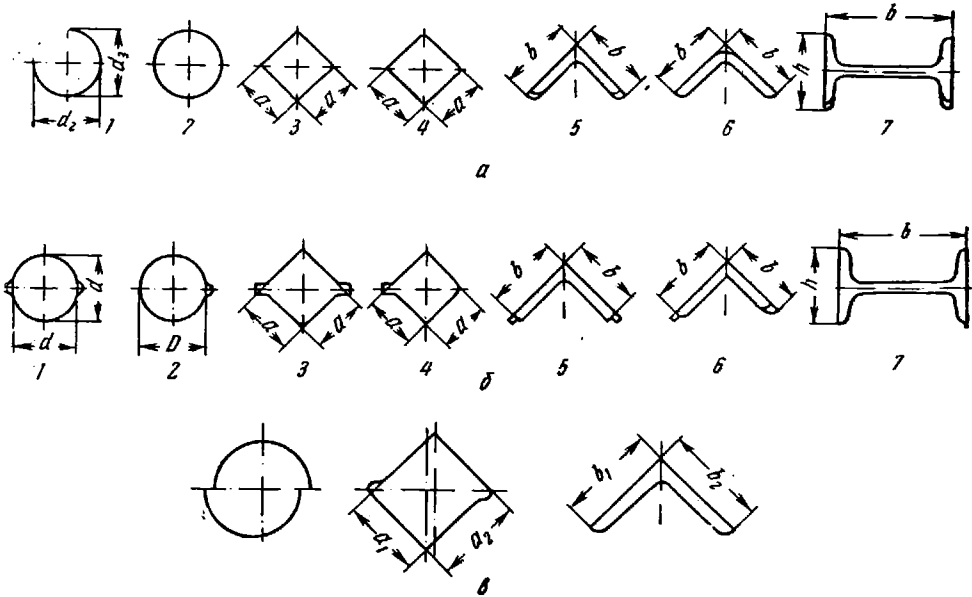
Виды дефектов профиля при прокатке сортовой стали
